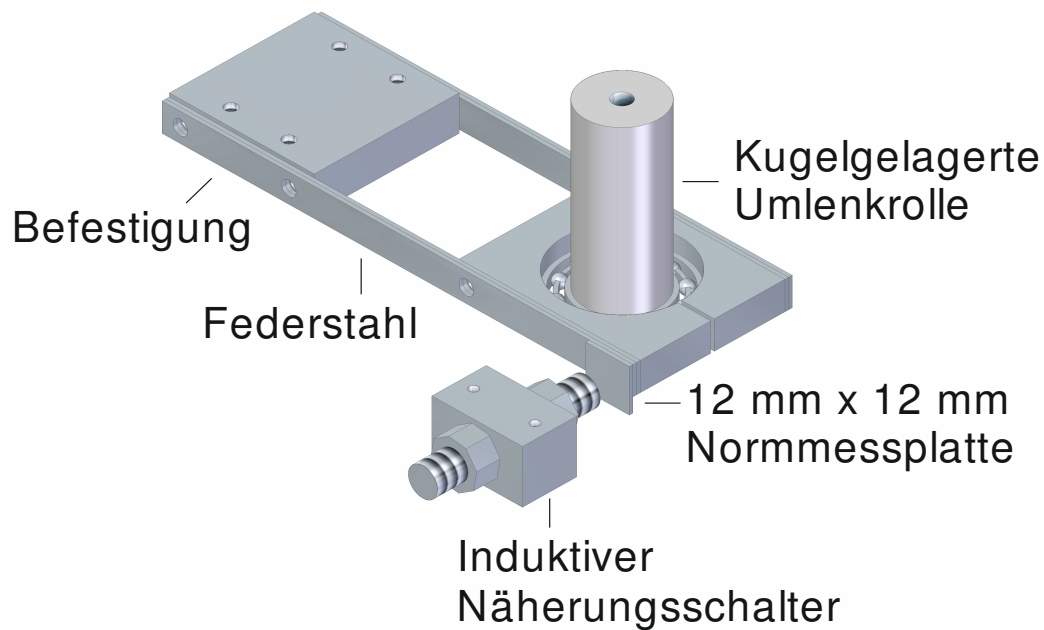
Kraftmesser mit induktivem Näherungsschalter für die Kraftmessung beim Umwickeln einer Klebebandrolle.
